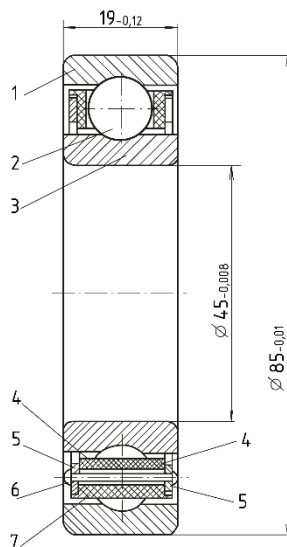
Типовая конструкция шарикового подшипника ТНА
